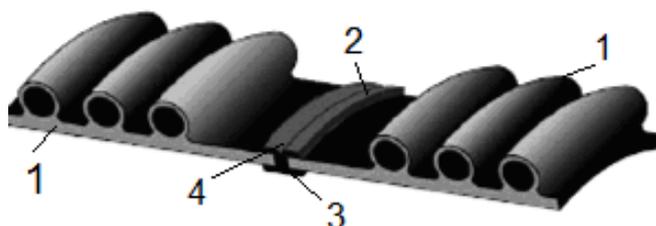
Фрагмент соединения спиральновитых из полых фигурного поперечного сечения профилей труб сваркой ЗН
